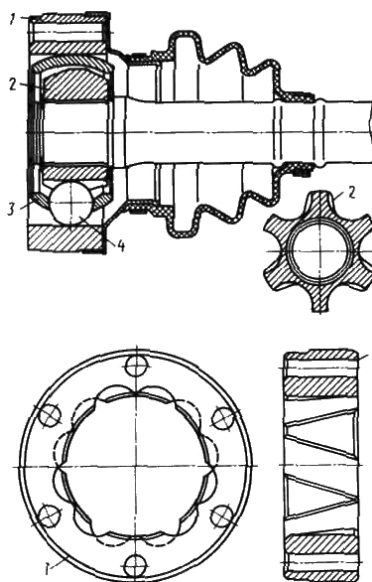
Карданный шарнир типа «Лебро»: 1 – цилиндрический корпус; 2 – сферический кулак; 3 – сепаратор; 4 – шарiki
